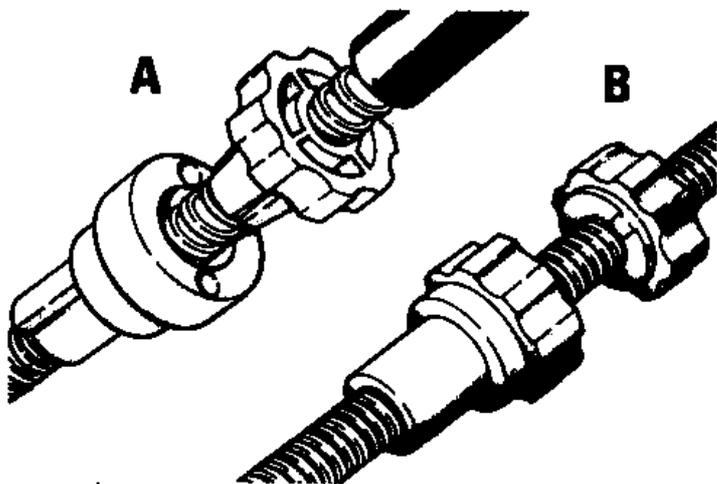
Два типа регулятора троса ручного тормоза (Разд.12)
